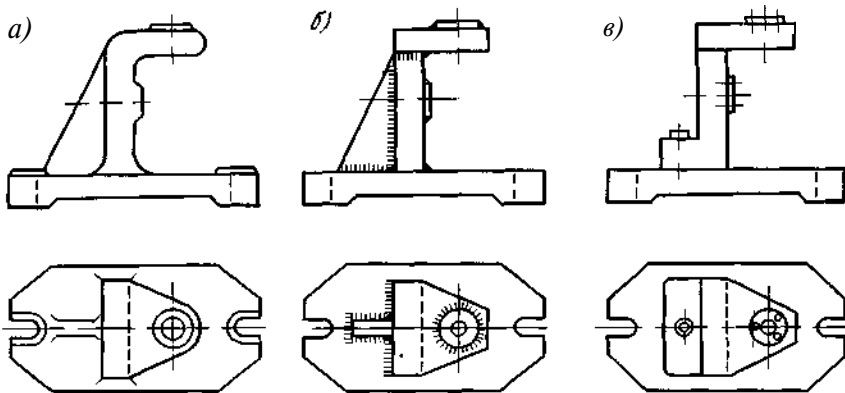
4 Технологические варианты конструкции корпусов приспособления
